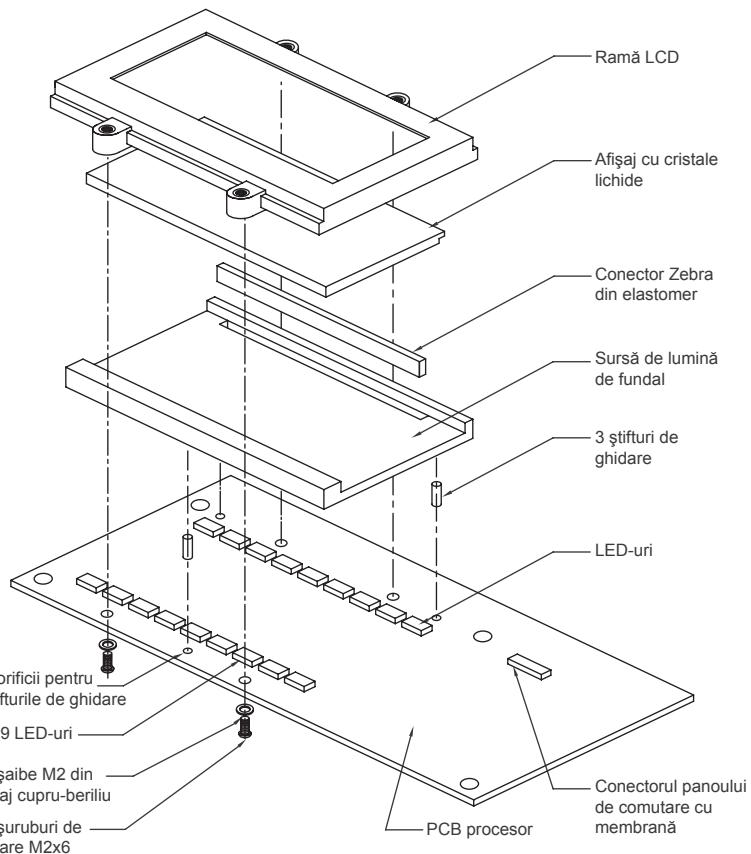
Vedere descompusă a ansamblului PCB procesor V3
